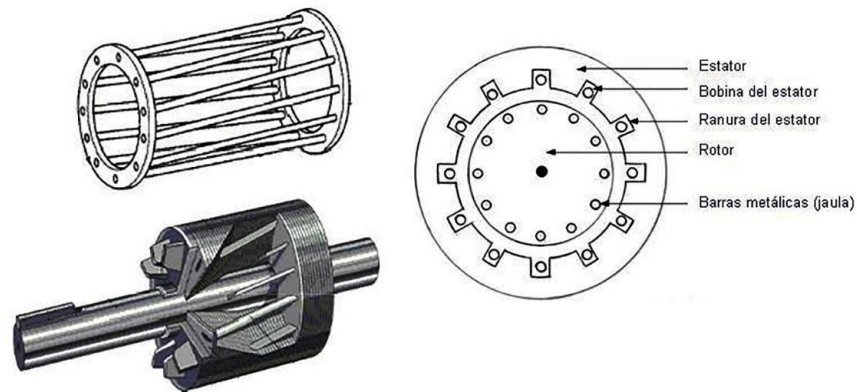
Partes básicas estator y rotor jaula de ardilla
